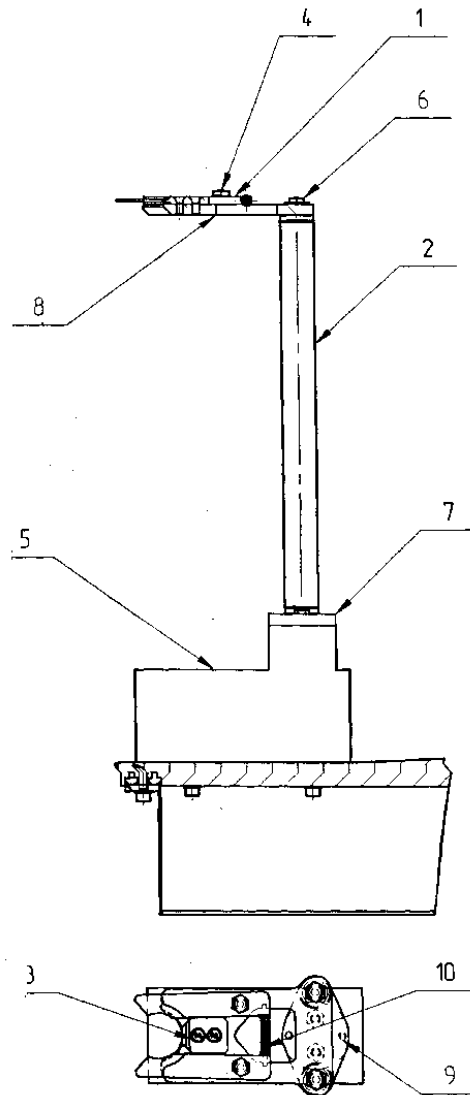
Захватний механізм розливного модуля триблока CGF32-24-8: 1 – затискачі; 2 – колонка; 3 – упор; 4 – болт спеціальний; 5 – ваговий давач; 6 – болт; 7 – опора; 8 – планка; 9 – штифт; 10 – пружина
